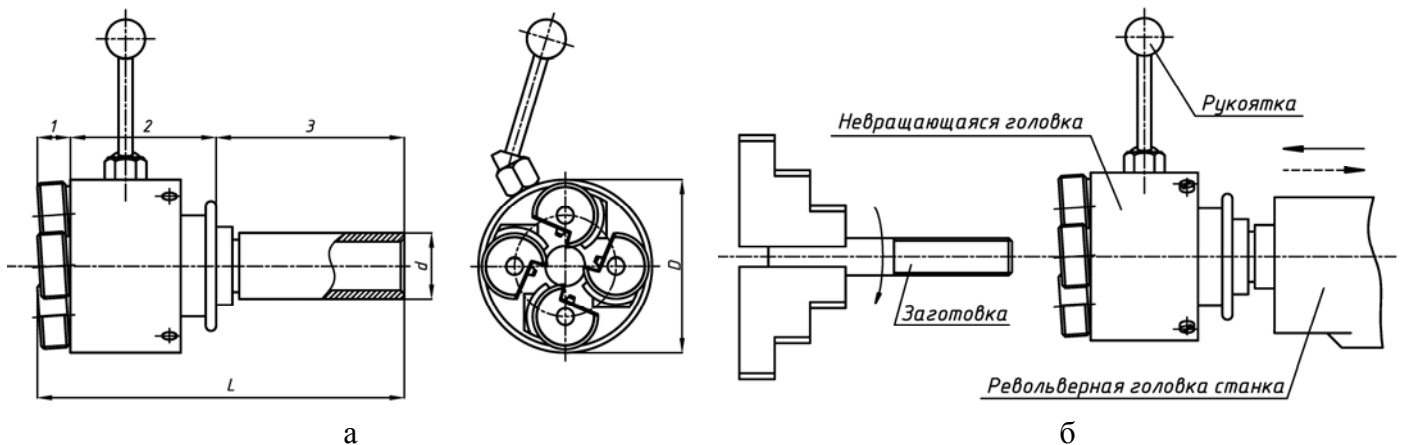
Невращающаяся резьбонарезная головка для наружной резьбы
